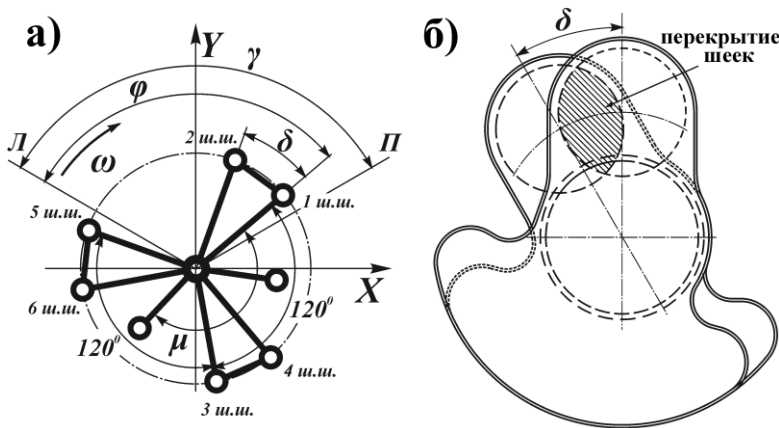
Схема 3-х коленного вала с разрезными шатунными шейками двигателя V6; $L, П$ – оси цилиндров левого и правого ряда; φ – текущий угол поворота кривошипа; γ – угол развала цилиндров; δ – угол смещения шатунной шейки; μ – угол установки дополнительного противовеса
